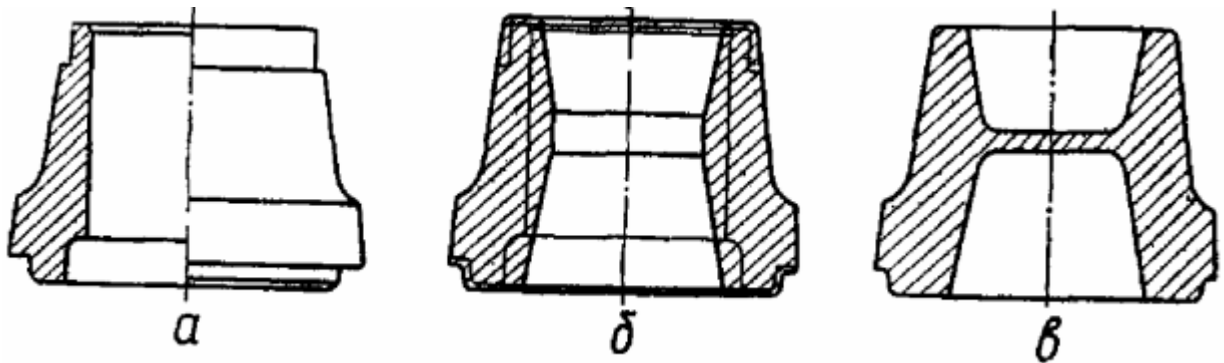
Креслення деталі (а) і штампованої заготовки для неї (б, в)
